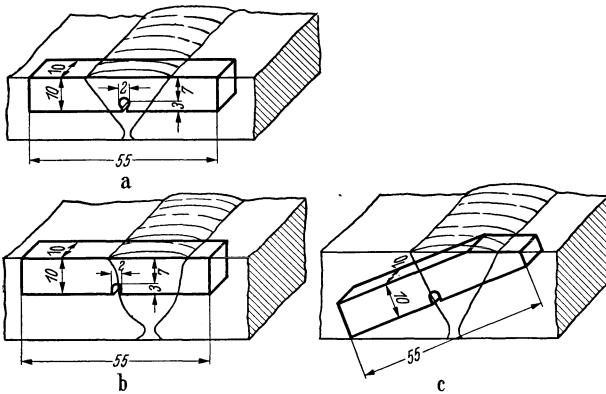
Kerbschlagproben und ihre Entnahmestellen an Schweißnähten.
